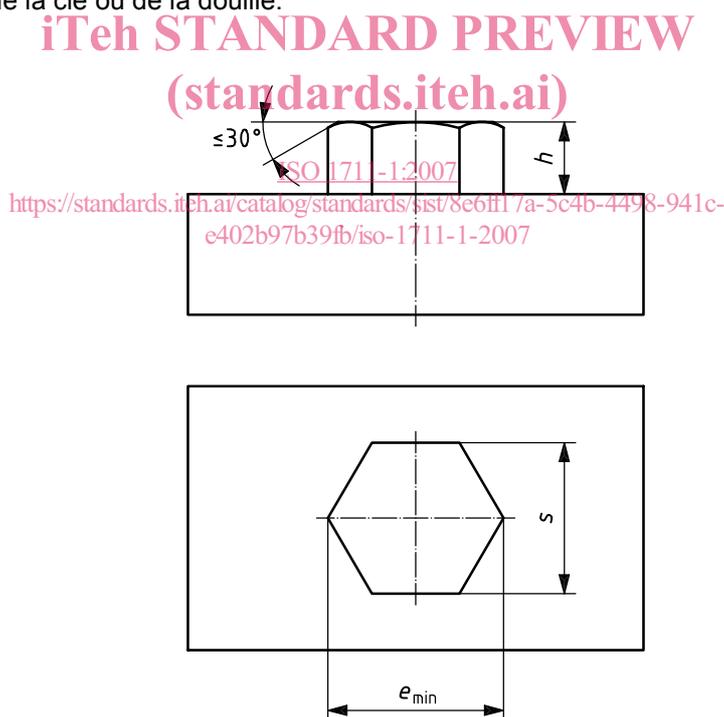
Hauteur, cote de surplats et surangles du mandrin d'essai
